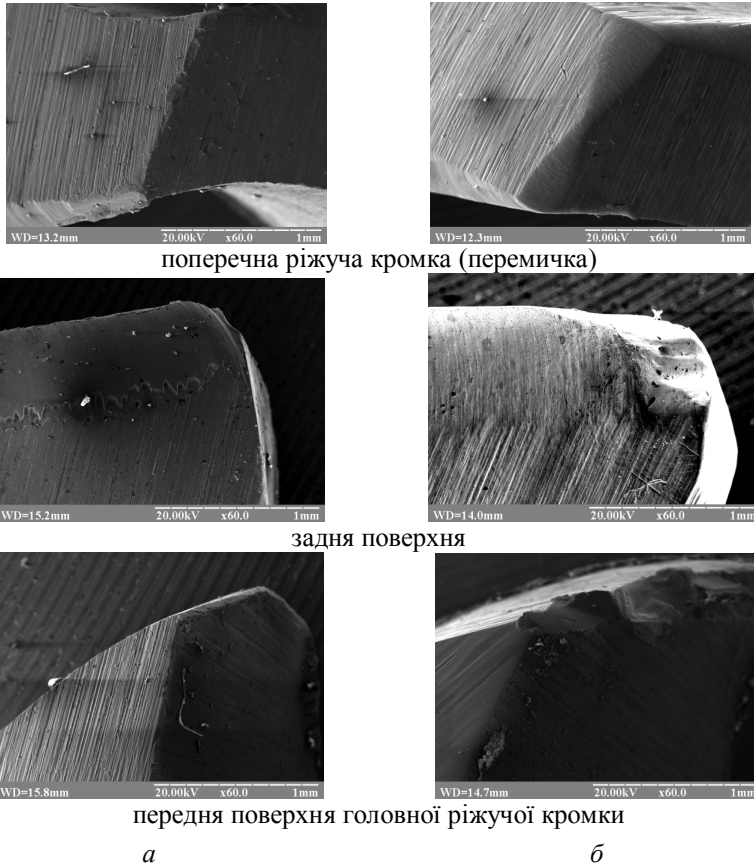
Фотографії робочих поверхонь свердел зі сталі Р6М5 після свердління композиційних матеріалів на основі поліетилену: *a* – робочі поверхні свердел зміцнені боруванням з наступною лазерною обробкою; *б* – робочі поверхні без обробки
